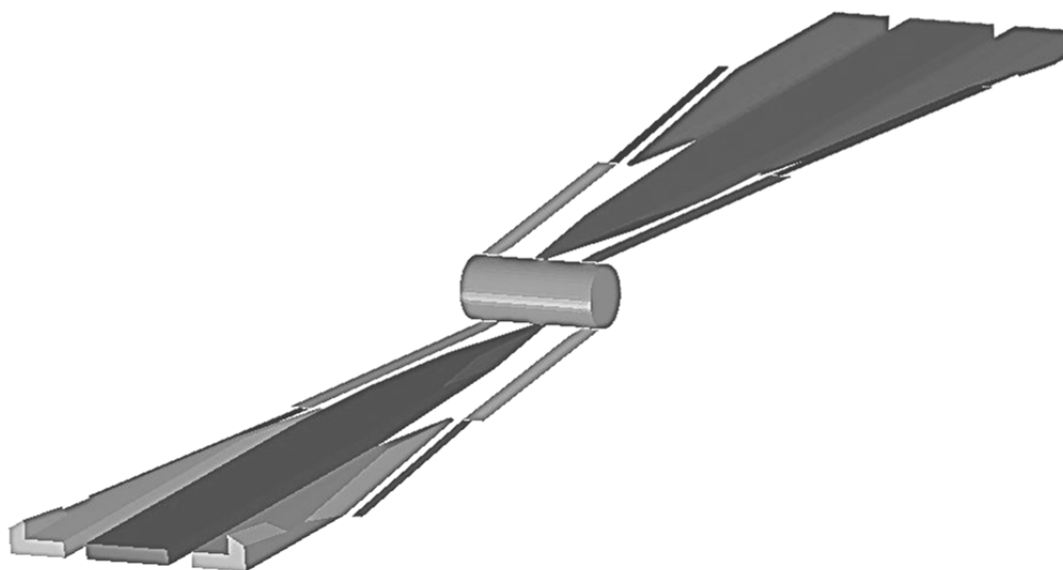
3d-модель инструмента и заготовки при плоской ПКП
